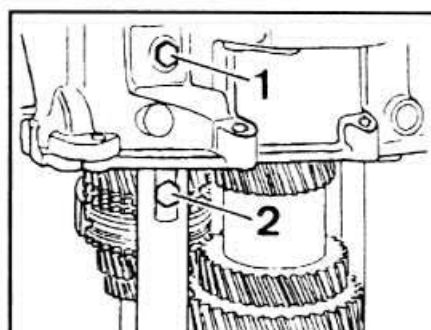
Болты 1 и 2 крепления оси промежуточной шестерни заднего хода
